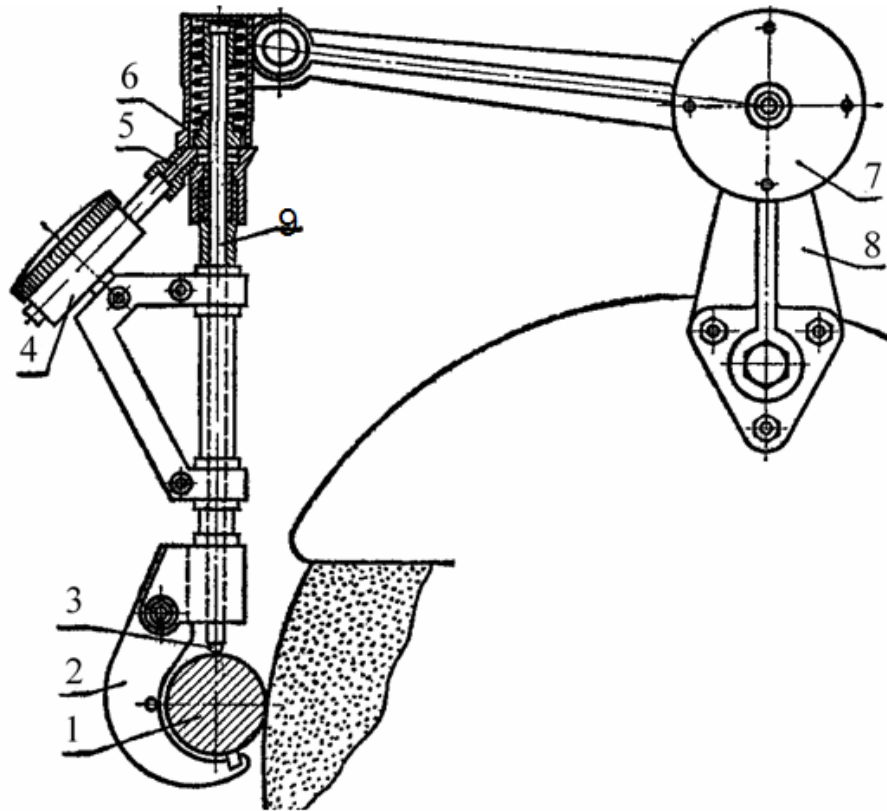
Пристрій для контролю розміру шийки вала в процесі шліфування: 1 – шийка вала; 2 – скоба; 3 – вимірвальний стрижень; 4 – індикаторна головка; 5 – ніжка індикатора; 6 – передавальний механізм; 7 – демпфер (масляний); 8 – встановлювальний кронштейн; 9 – стрижень передавального механізму
